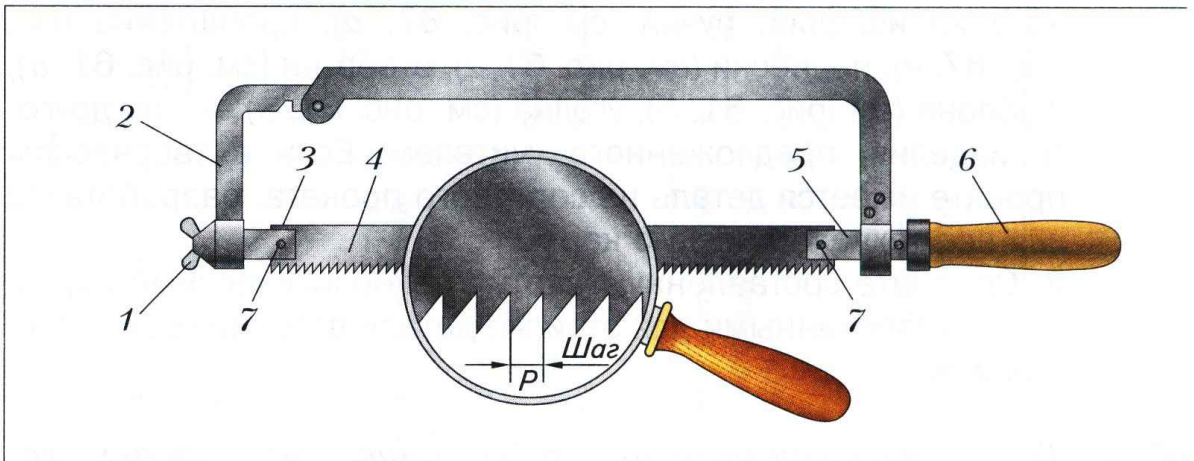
Ручная слесарная ножовка: 1 – гайка; 2 – рамка; 3 – подвижная головка; 4 – ножовочное полотно; 5 – неподвижная головка; 6 – хвостовик с ручкой; 7 – штифты
